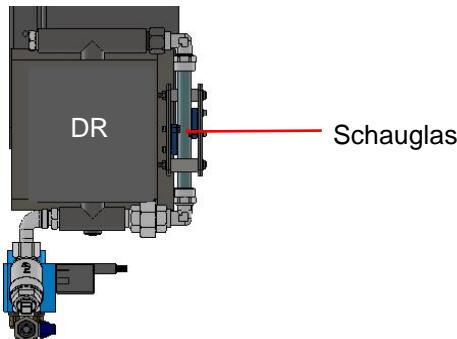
Schauglas für den Wasserstand vom Dampferzeuger
